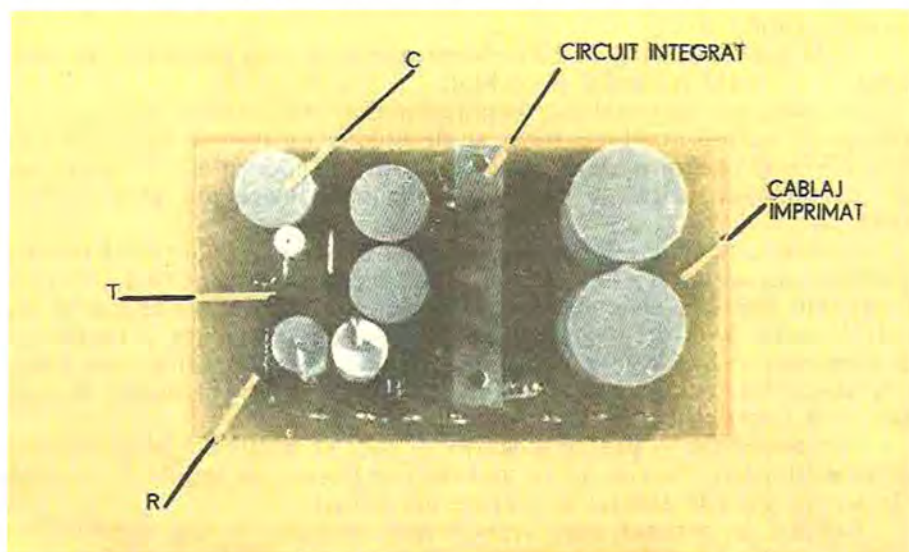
Cablaj imprimat echipat cu componente electronice.
